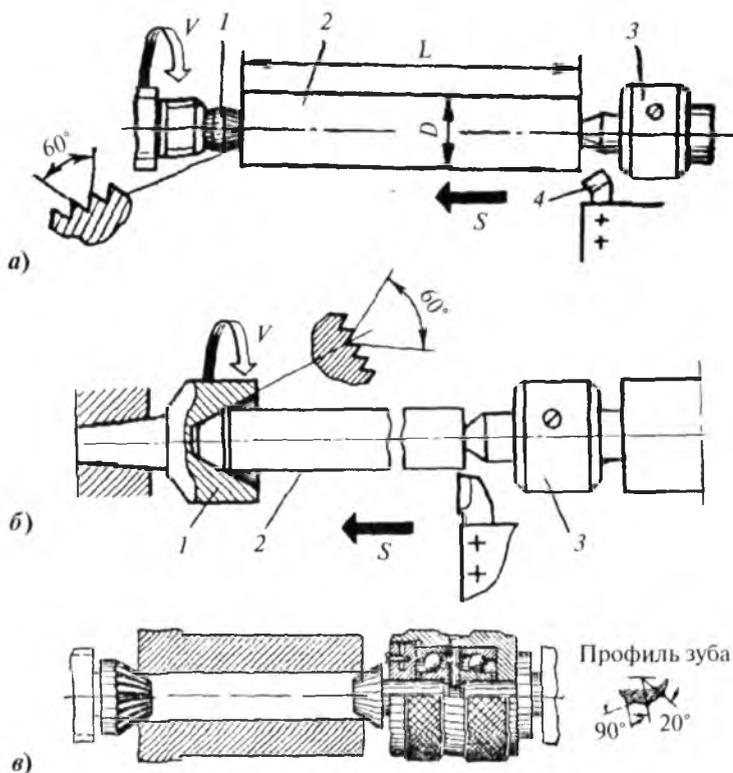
а, б — пример закрепления прутка в центрах: 1 — передний центр; 2 — заготовка; 3 — задний центр; в — закрепление втулки в грибовых центрах
